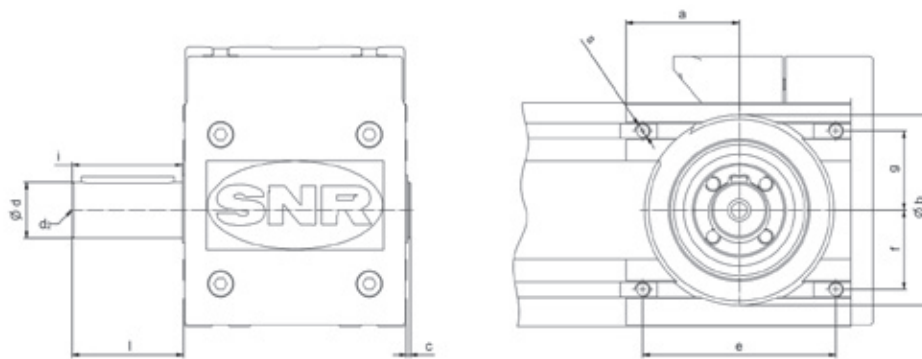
Abmessungen Steckwelle und Anbaumaße
